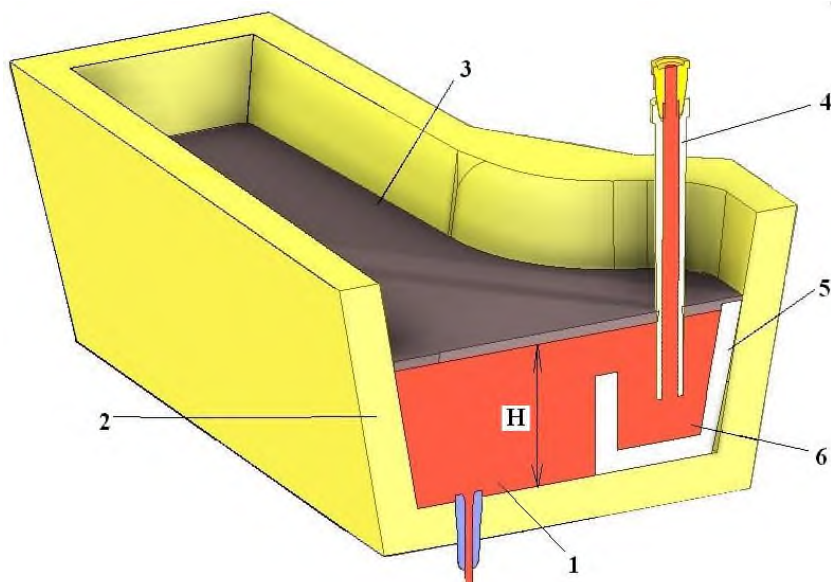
Модель оборудования для определения параметров расположения потоков стали: 1 – ньютоновская жидкость - металл; 2 - борт; 3 – защита поверхности металла; 4 – поток в направляемой защите; 5 – конструкция для приема металла; 6 – часть ковша для расположения струи стали из сталеразливочного ковша; H – номинальное положение жидкости в ковше
